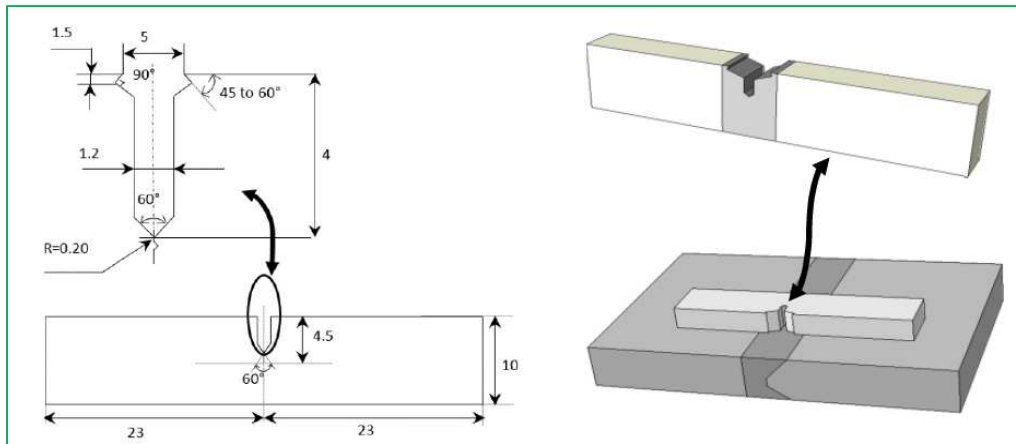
Dimensions des éprouvettes SENB in mm.
